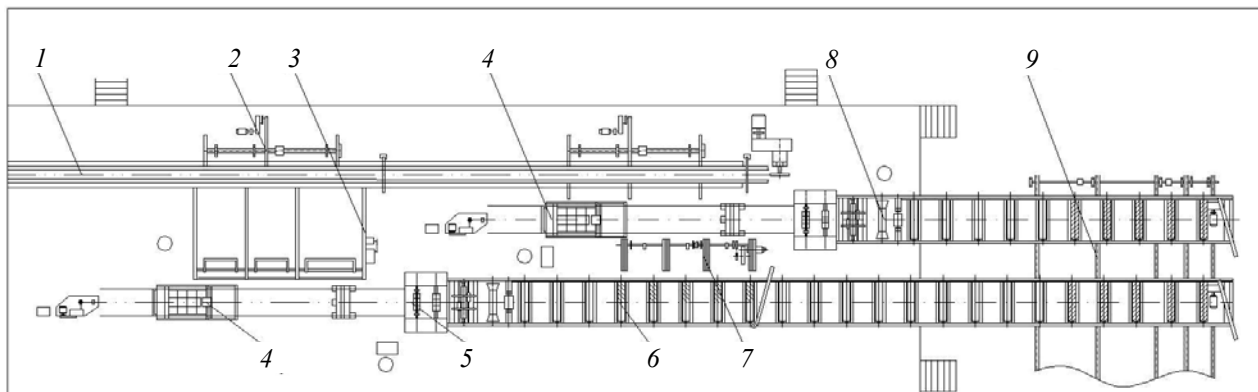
Схема лесопильного цеха на базе одноэтажных лесопильных рам:
